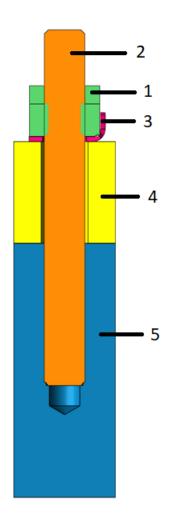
Вид в разрезе: 1 – гайка, 2 – шпилька, 3 – шайба, 4 – пластина, 5 – деталь с глухим отверстием
